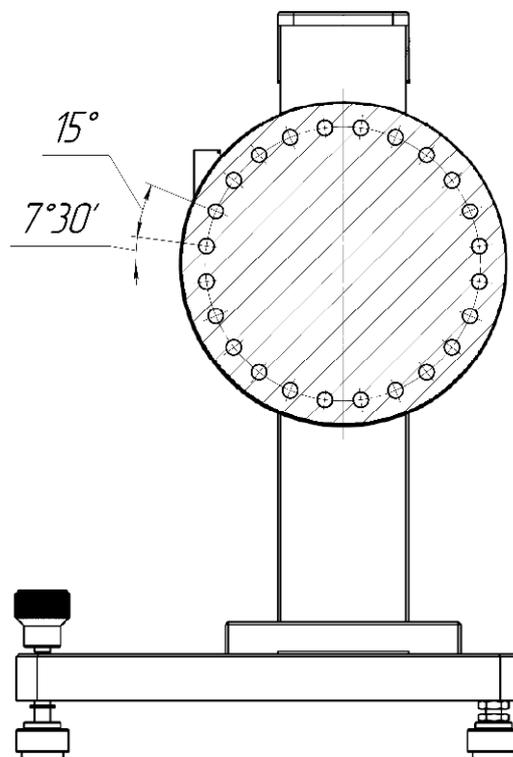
Чертеж установки для поверки систем лазерной центровки PRÜFTECHNIK CALI-CHEK Ti. Вид спереди
